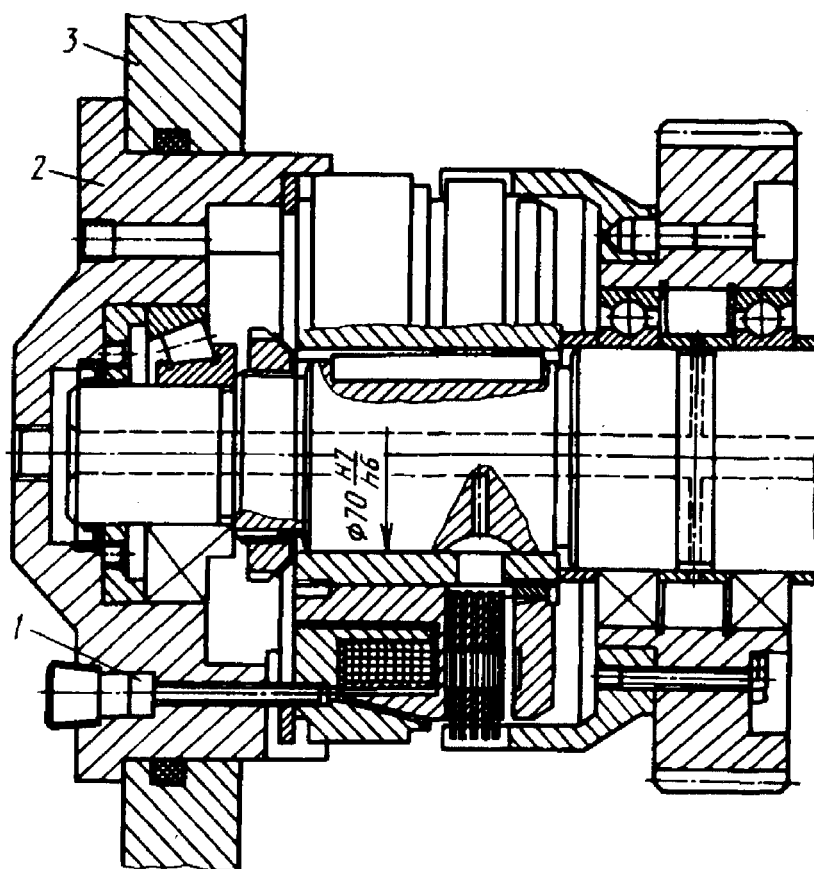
12. Пример встройки электромагнитной муфты Э1М...4 в механизм 1 - винт ; 2 - крышка ; 3 – корпус
